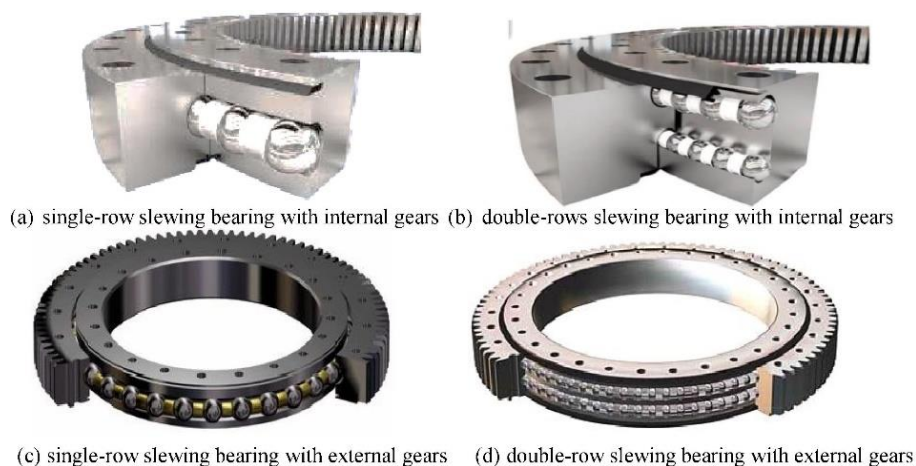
风电机回转轴承^[12]: (a) 带内齿轮的单列回转轴承; (b) 带内齿轮的双列回转轴承;
